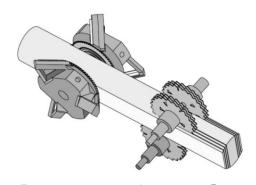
Схема работы фрезернопильного оборудования
